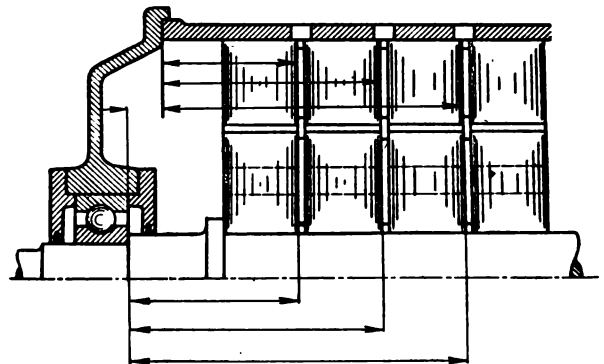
Шихтовка сердечников с радиальными каналами.
